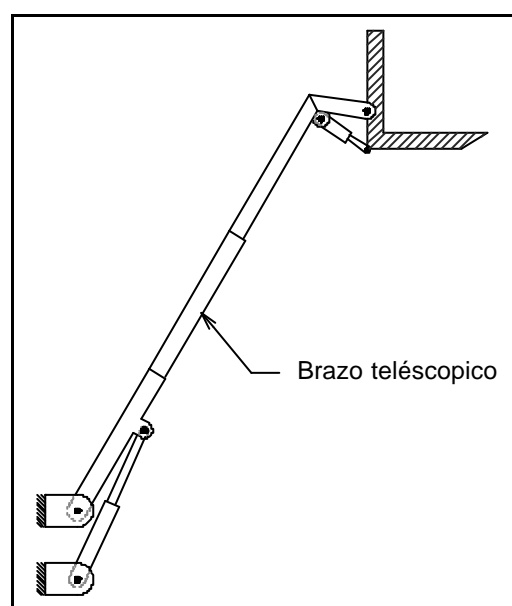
Mecanismo de elevación con brazo telescópico
